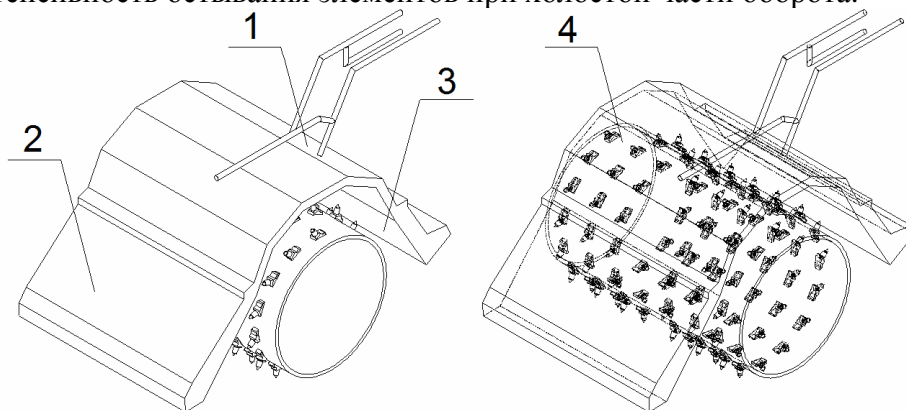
Фрезерно-смесительный агрегат: 1 – рампы распределения; 2 – задняя стенка; 3 – передняя стенка; 4 – фрезерный барабан
